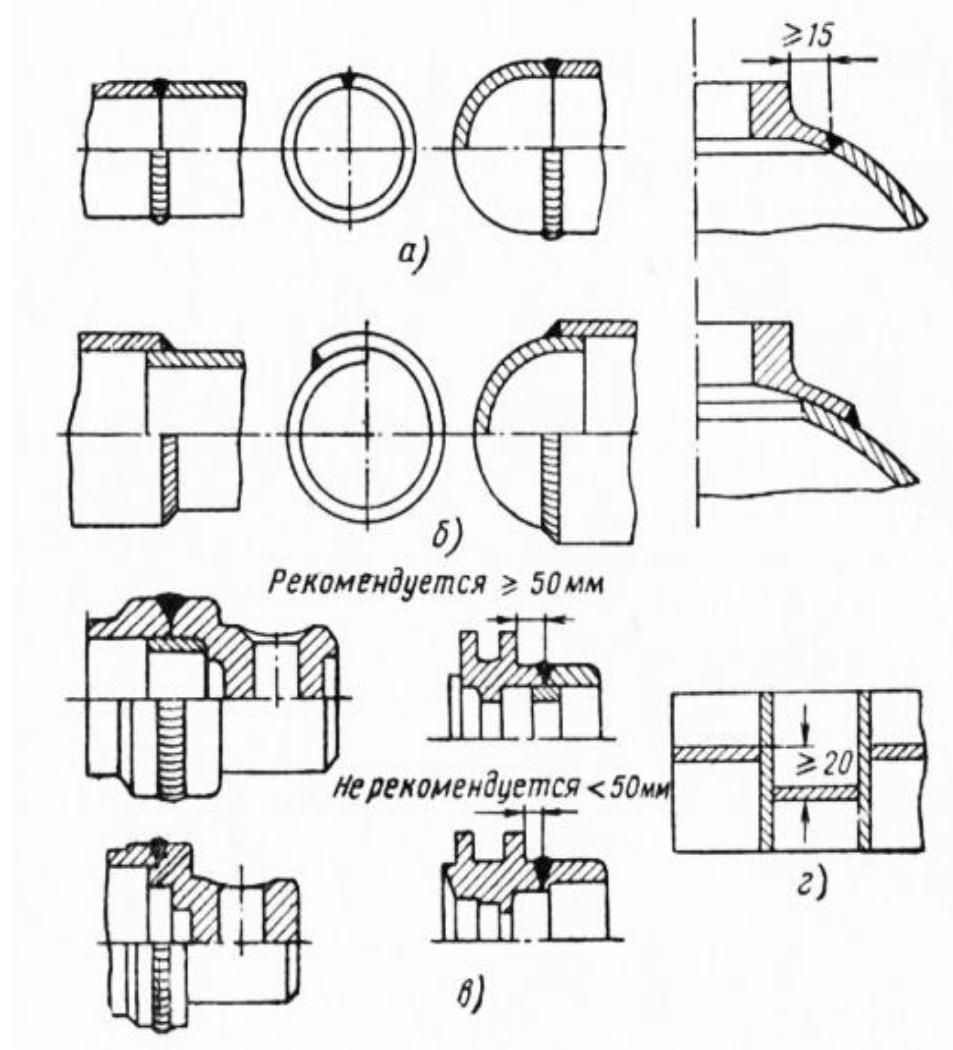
Примеры технологичных и нетехнологичных конструкций сварных узлов, выполняемых сваркой плавлением
